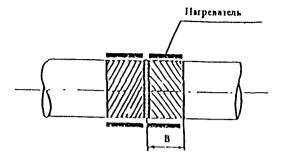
Схема нагрева труб перед сваркой: В - ширина зоны нагрева
